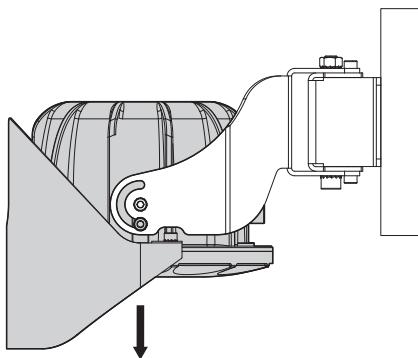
Монтаж на стену (вертикальное перемещение, -90°).
